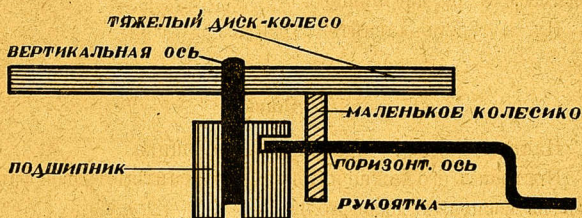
Схема приспособления механизма, приводящего в движение пластинку.
